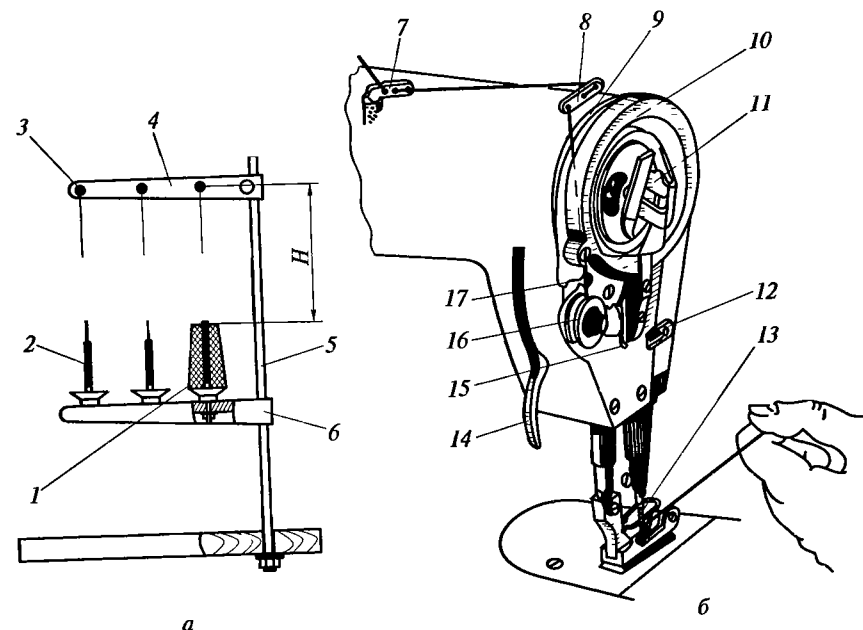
Схема заправки игольной нитки на швейной машине класса 97-А: а — установка бобины; б — заправка игольной нитки
